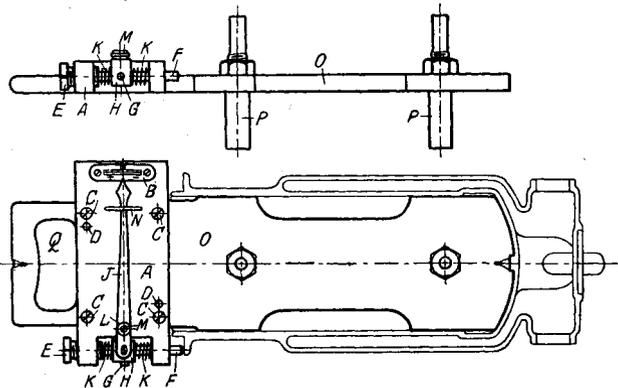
u. 96. Fühlhebellehre für Motorzylinder.
